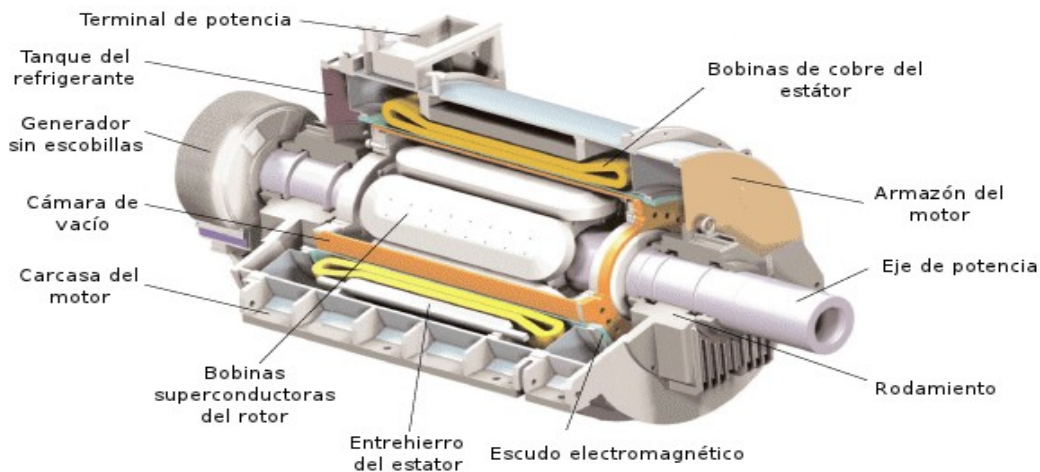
Corte longitudinal del motor superconductor de 5 MW de AMSC (Fuente: AMSC; imagen adaptada por el autor)
